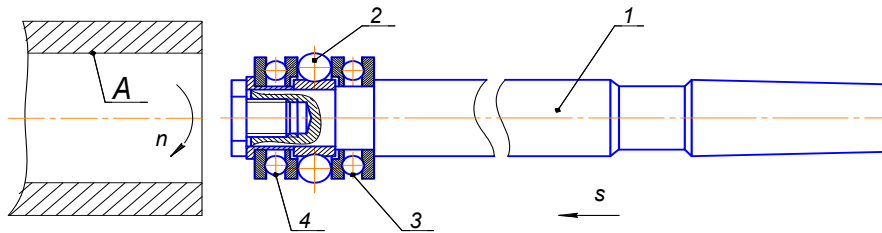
Конструкція кулькового інструмента для розкочення внутрішніх циліндричних поверхонь
